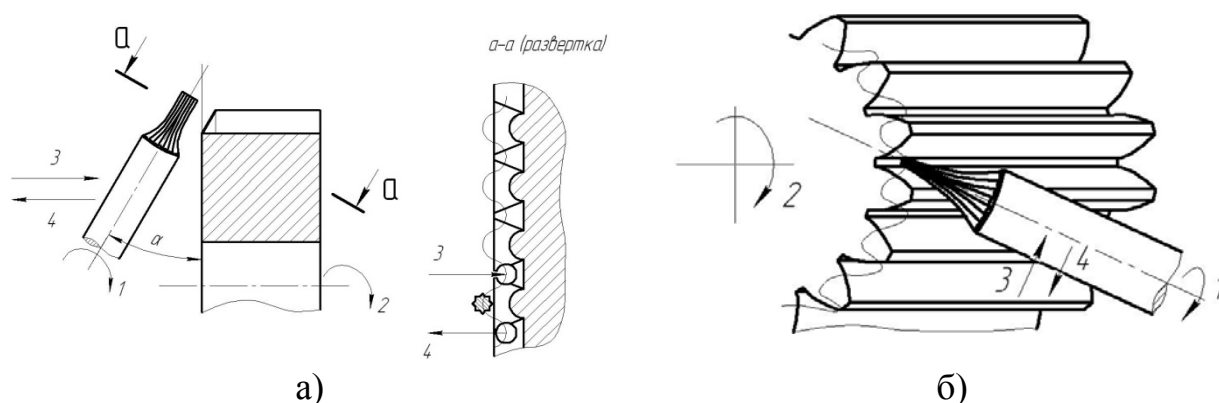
Процесс бочкообразного закругления зубьев:
